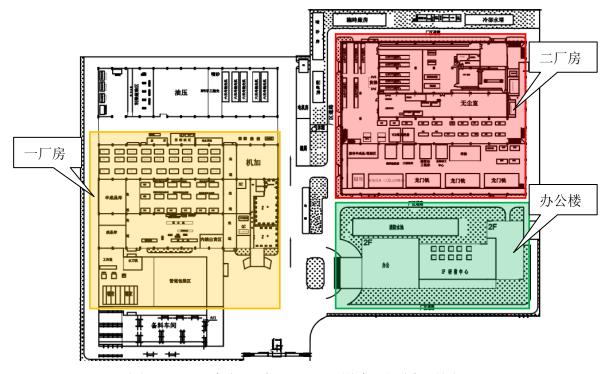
陆丰西路厂区 1 层设备平面布置图
